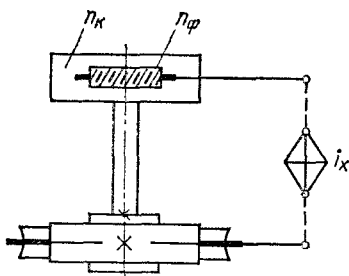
Принципиальная схема настройки зубофрезерного станка
